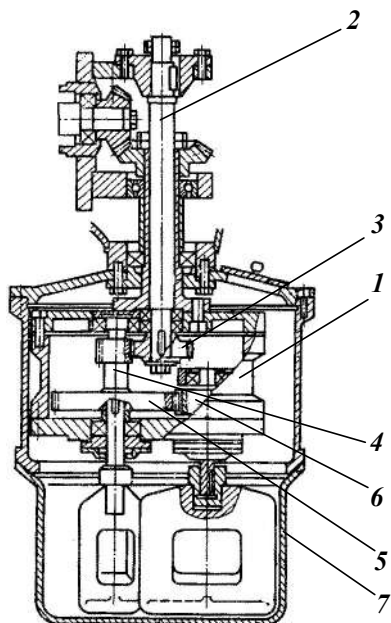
Смеситель планетарно-лопастного типа: 1 – планетарный редуктор; 2 – неподвижный вал; 3 – неподвижное зубчатое колесо; 4 – вал; 5 – тихоходное зубчатое колесо; 6 – быстроходное зубчатое колесо; 7 – чаша.
